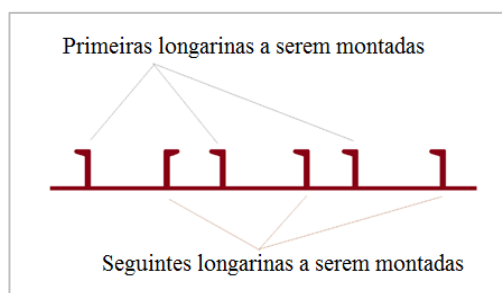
Sequências de montagem de longarinas, através de pingos de soldadura (Fonte: West-sea)
